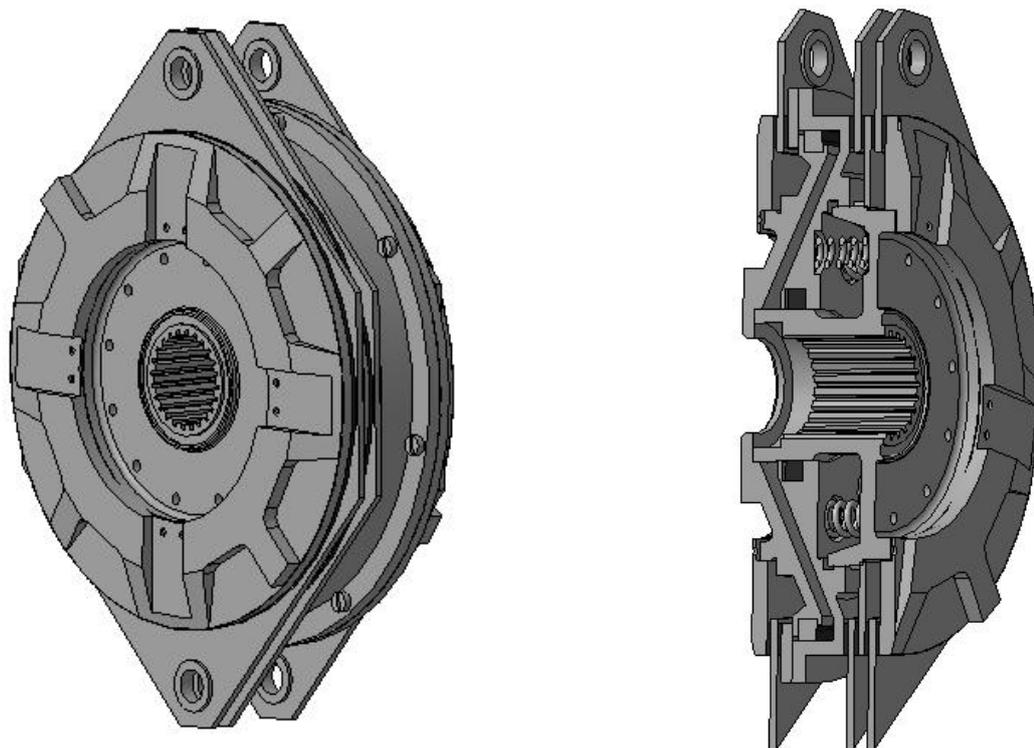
Сборочная 3D-модель узла пресса «Муфта-тормаз»
